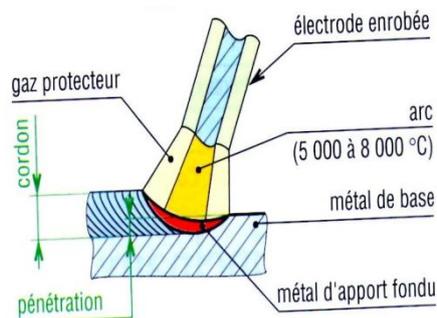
Principe du soudage à l'arc. [8]
